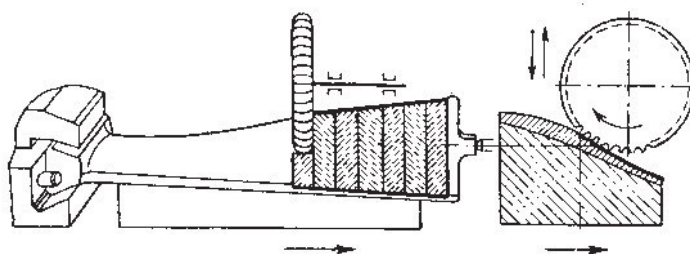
Схема роздільного фрезерування корита і спинки пера лопатки широкими поперечними строчками.
